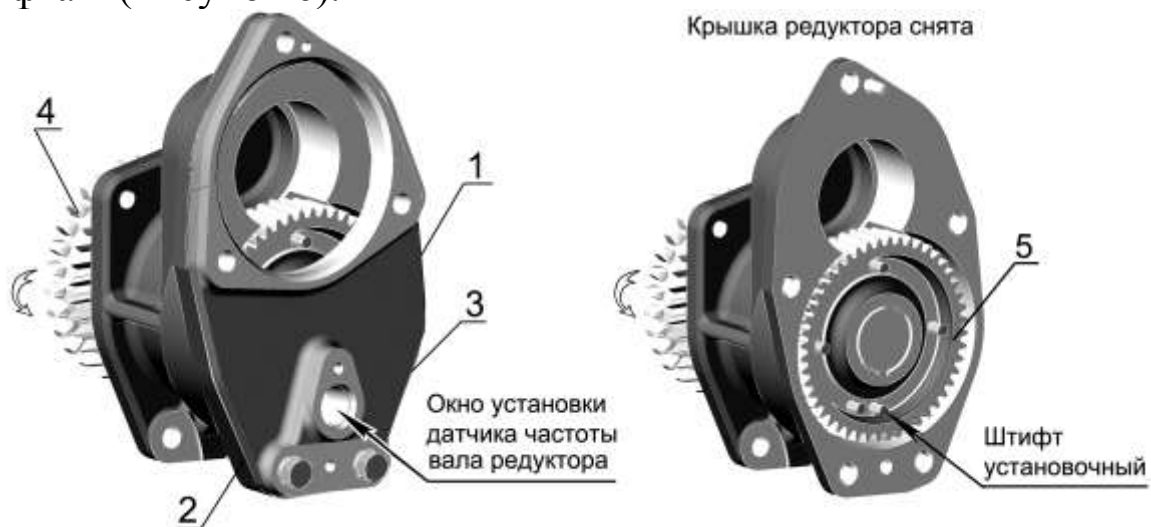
Редуктор привода ТНВД: 1 – редуктор привода ТНВД; 2 – установочный фланец датчика; 3 – болт крепления фланца; 4 – шестерня привода редуктора; 5 – шестерня с импульсными штифтами
